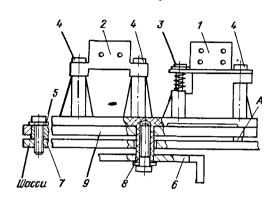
Установка магнитных головок и крепление ползуна ЛПМ
